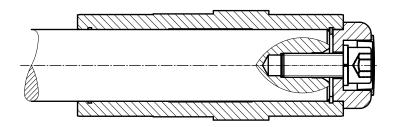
Getriebe auf Welle ohne Anlageschulter mit Befestigungselement befestigt
